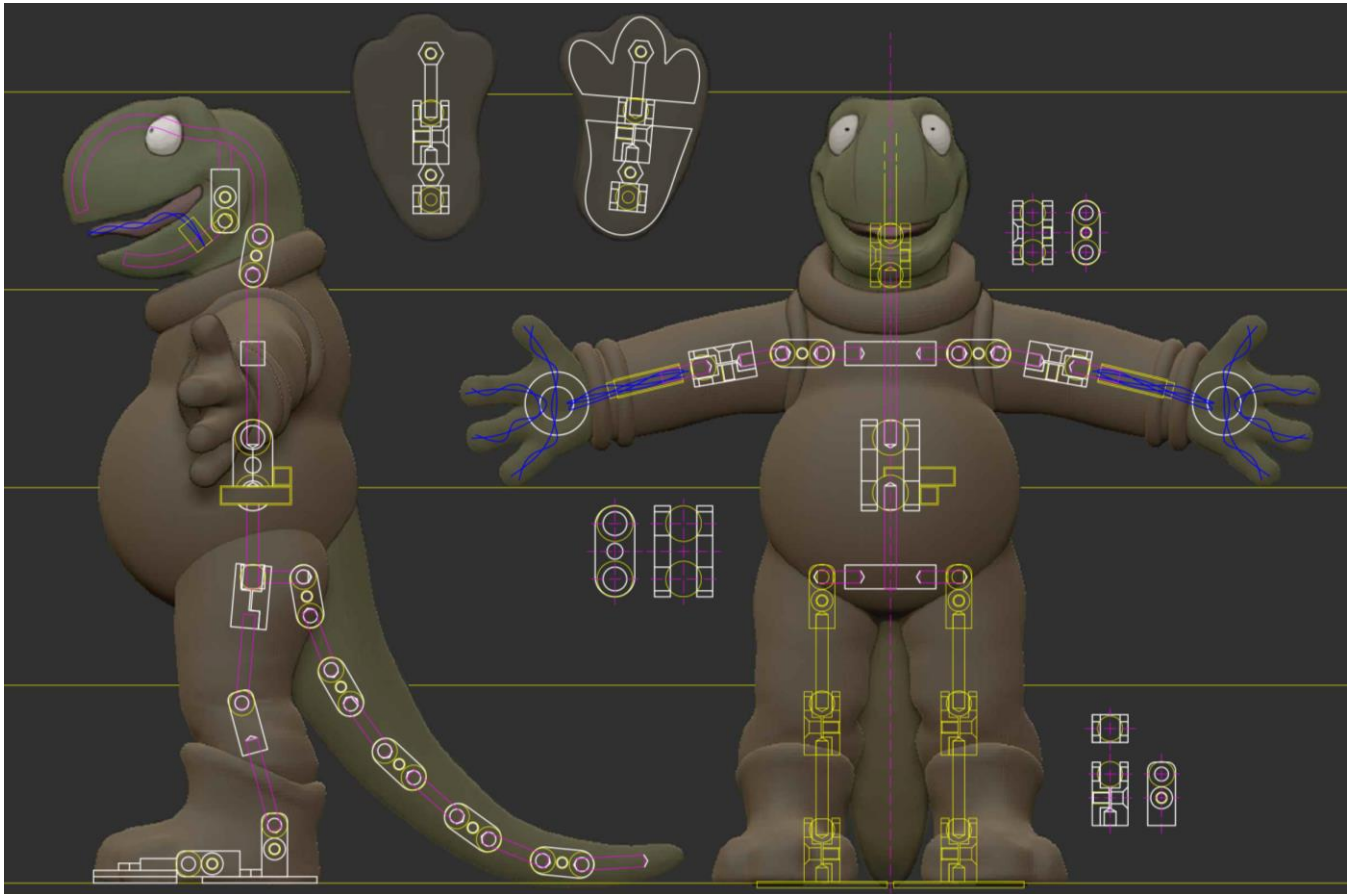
· Plano técnico de conjunto. Vistas lateral y frontal. Realizado en Autocad.
